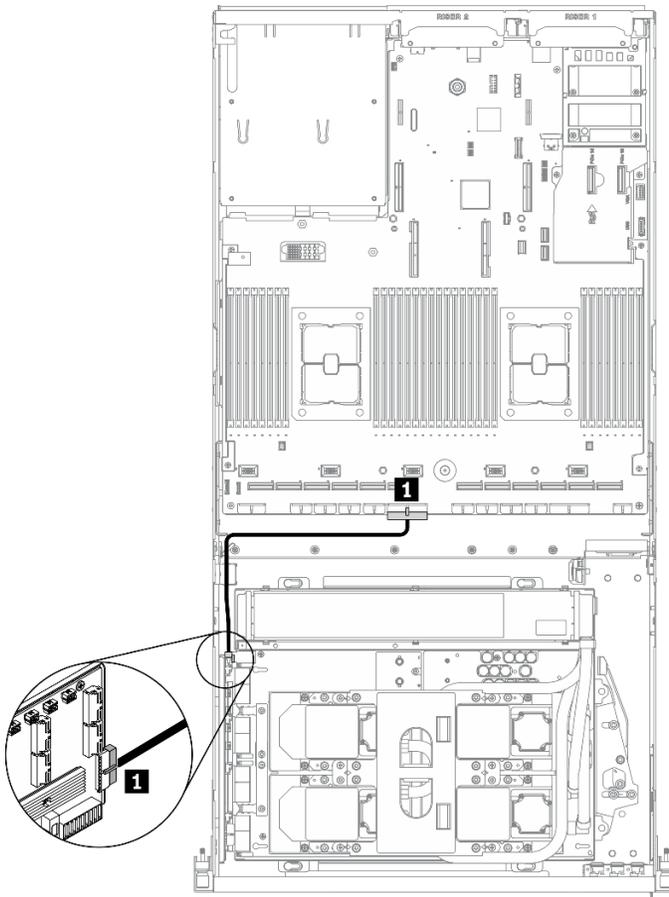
Instradamento dei cavi dell'assieme retimer (cavo di alimentazione) - Configurazione F
